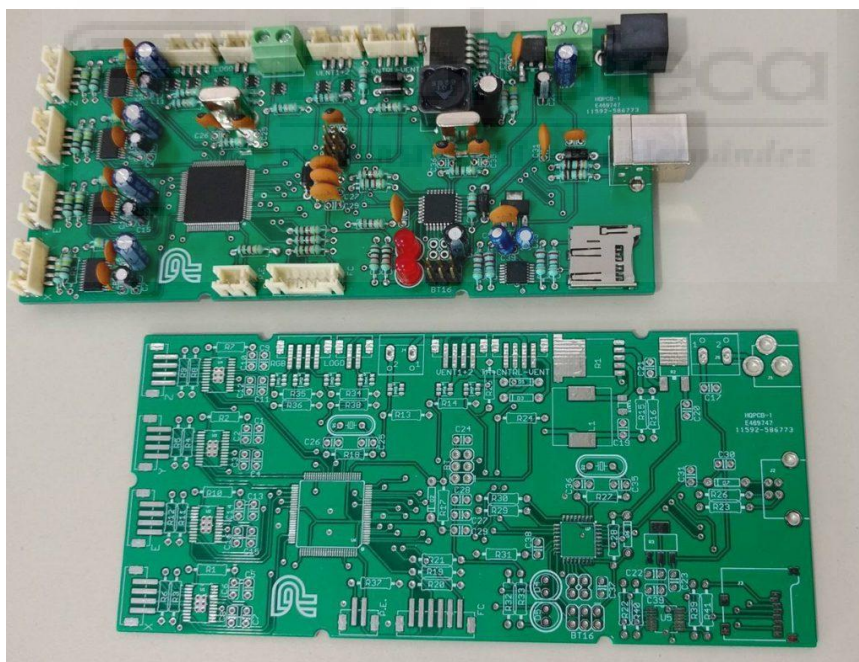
Placa de circuito impreso. Fuente: PCB central (2019).
